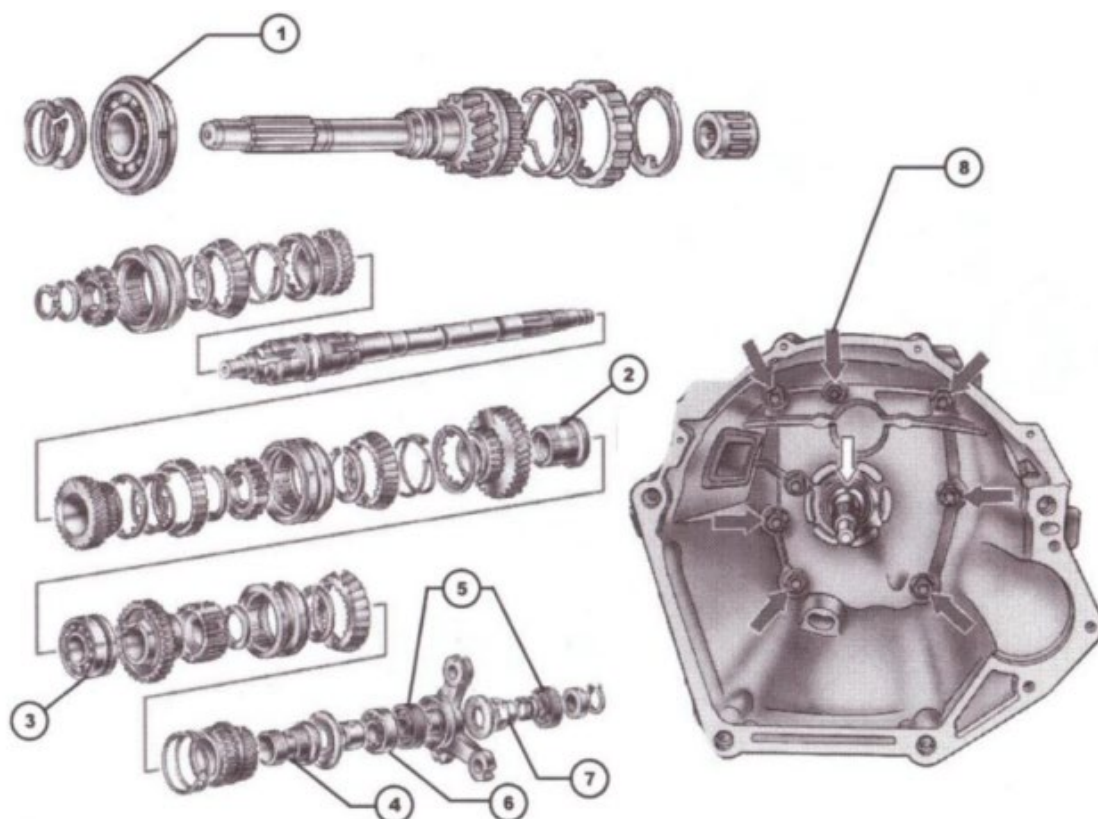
Відновлення нерухомих з'єднань адгезивами в коробці передач: 1 – фіксування підшипника первинного валу; 2 – фіксування втулки шестерні вторинного валу; 3-фіксування підшипника вторинного валу; 4 – фіксування втулки шестерні вторинного валу; 5 – ущільнення та фіксування сальника; 6 -фіксування підшипника вторинного валу; 7 – стопоріння гайки; 8 – стопоріння гайок картера зчеплення
